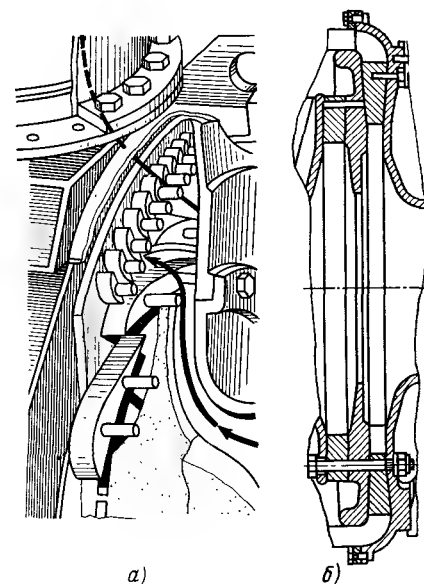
Лопаточные диффузоры напорных патрубков центробежных компрессоров:
